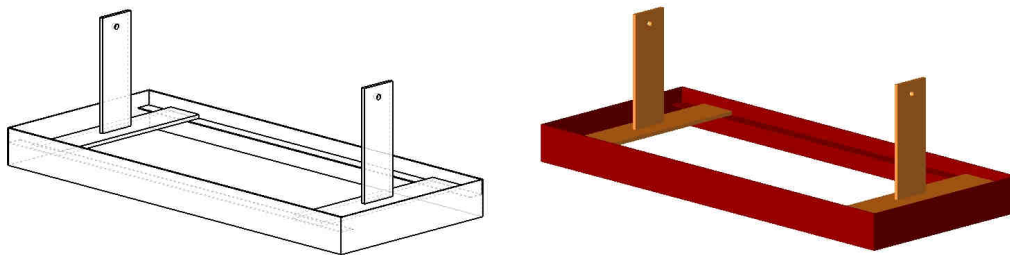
Diseño de soportes sobre base general de la máquina de rotomoldeo.
